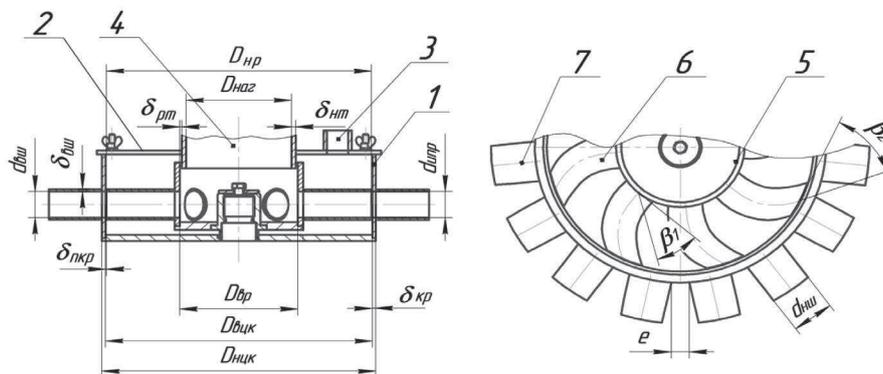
Схема для обоснования конструктивных и кинематических параметров роторного распределителя: 1 – цилиндрический корпус; 2 – крышка; 3 – сапун; 4 – нагнетательный трубопровод; 5 – стакан ротора; 6 – патрубок ротора; 7 – выливной штуцер
